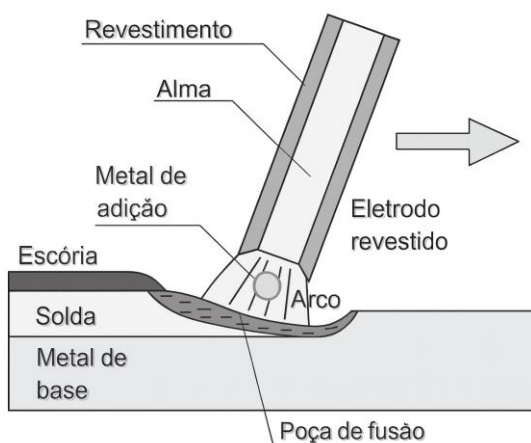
Desenho esquemático de uma soldagem com eletrodo revestido.
